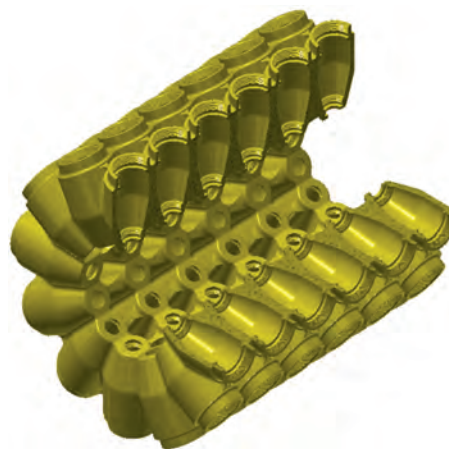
Целый корпус отсека импульсных твердотопливных ракетных двигателей
